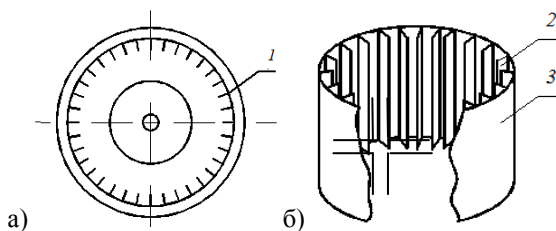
Схематичне зображення робочої камери пристрою попередньої підготовки зерен сої:
